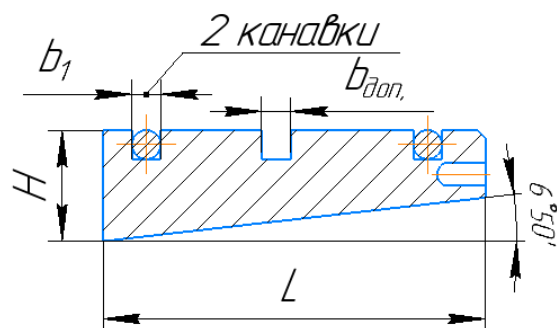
Эскиз кулачка оправки. Показана дополнительная канавка посередине для размещения разрезного кольца при обточке по месту
